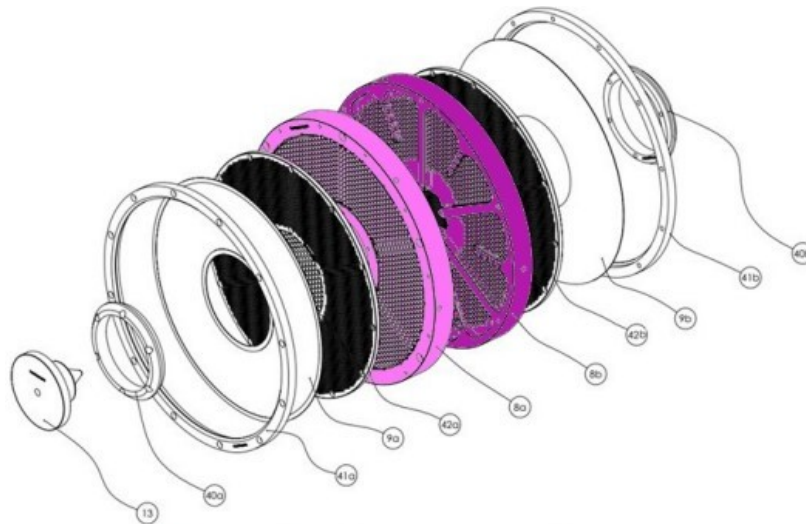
Explosionszeichnung des Filtereinsatzes
